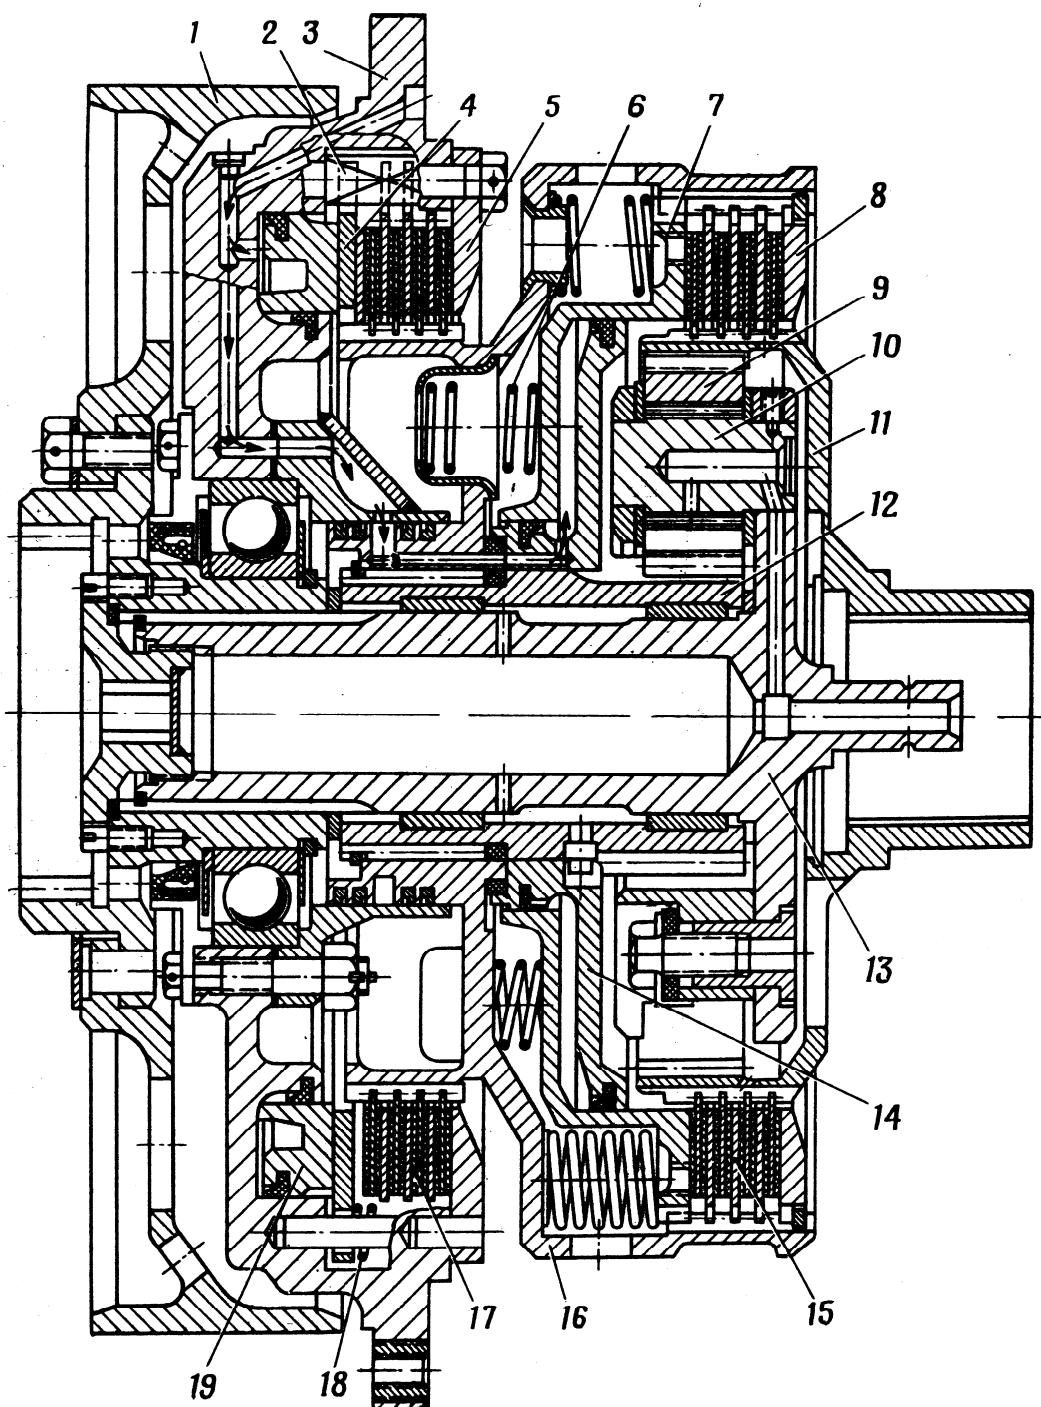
Планетарный редуктор механизма поворота боевой машины пехоты: 1 - барабан остановочного тормоза; 2 - призматическая шпонка; 3 - крышка; 4, 7 - нажимные диски; 5, 8 - опорные диски; 6 - пружина; 9 - сателлит; 10 -
